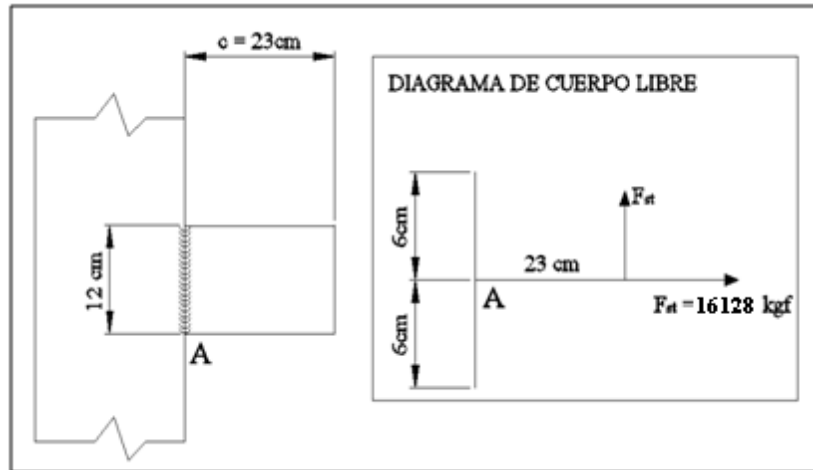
Esfuerzos de flexión de la soldadura
